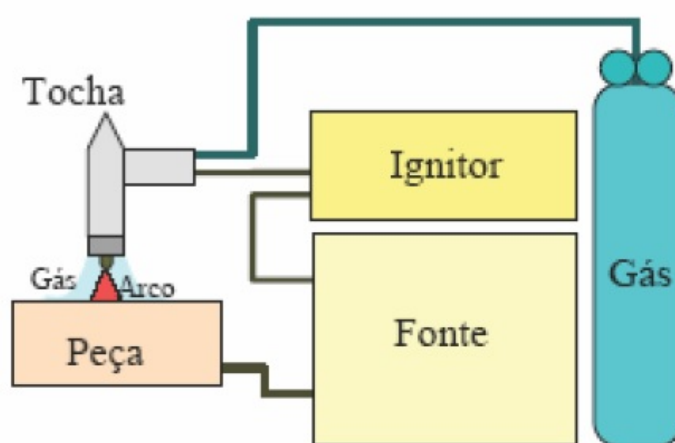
Equipamentos utilizados no processo de soldagem TIG. Fonte: adaptado de (MARQUES, 2011)
